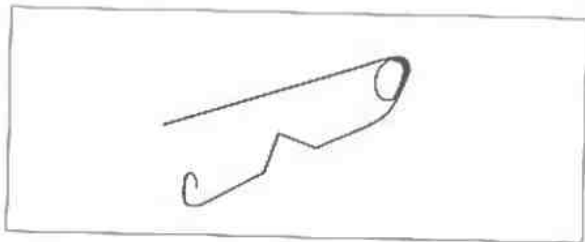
Схема изгиба булавки при изготовлении застежки броши
